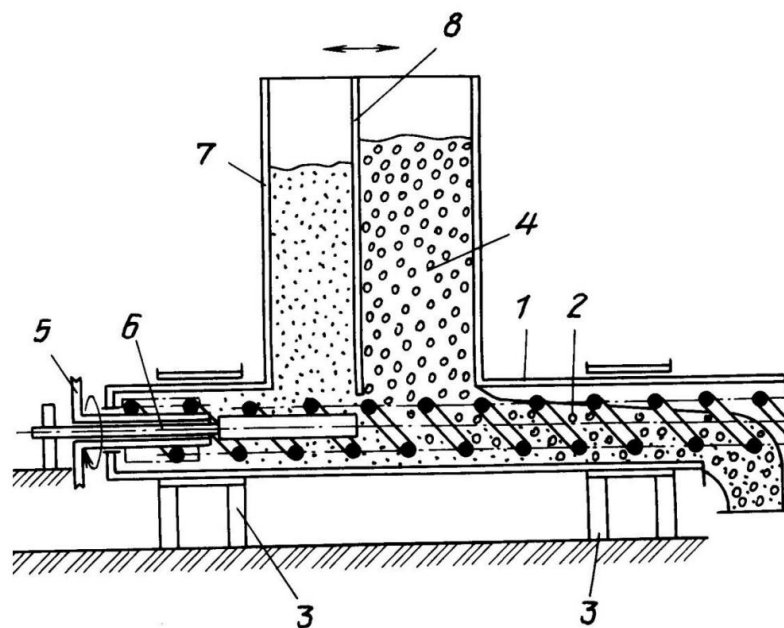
Дозатор-змішувач: 1 - циліндричний кожух; 2 – спіраль; 3 – опори; 4 - приймальне вікно; 5 - приводний шків; 6 – вкладиш; 7 – бункер; 8 – перегородка
